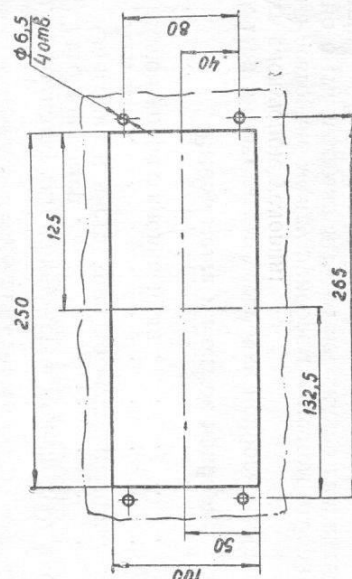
Габаритный чертеж мембранного профильного тягонапоромера.
